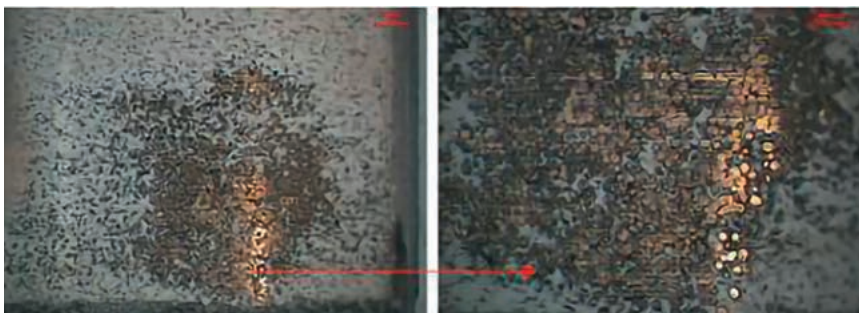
Forte usura locale conseguente ad un errore di montaggio
